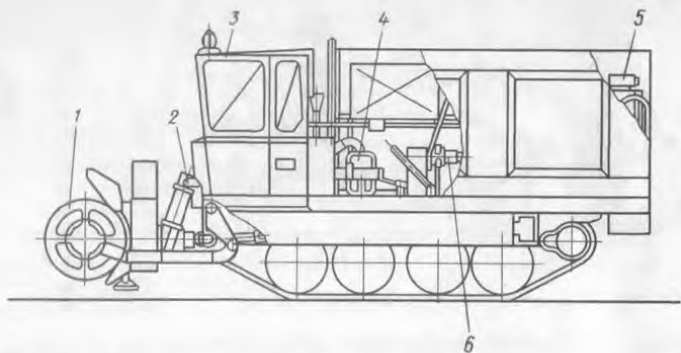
Фрезерно-роторный снегоочиститель ДЭ-212С
